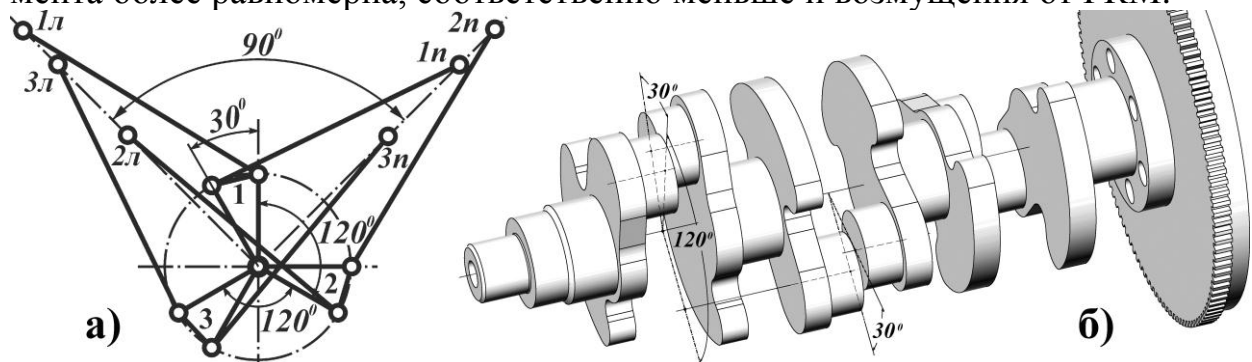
КШМ двигателя V6: а) схема КШМ V-образного 6-ти цилиндрового ДВС с равномерным чередованием рабочих ходов; б) коленчатый вал со смещенными шатунными шейками V-образного 6-тицилиндрового ДВС
